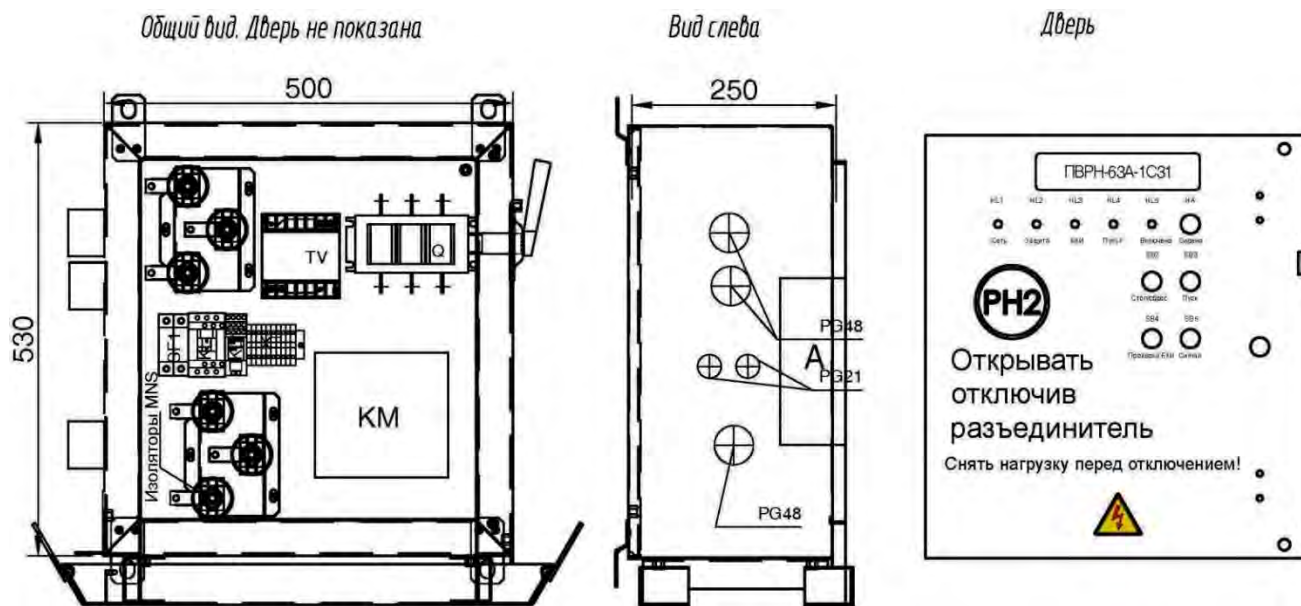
Общий вид ПВРН с габаритными размерами
